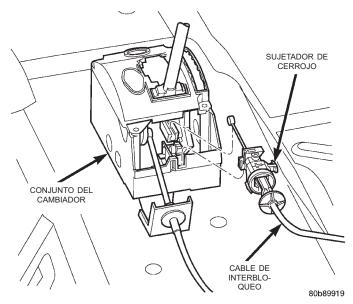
Cable de interbloqueo en el conjunto del cambiador de suelo
